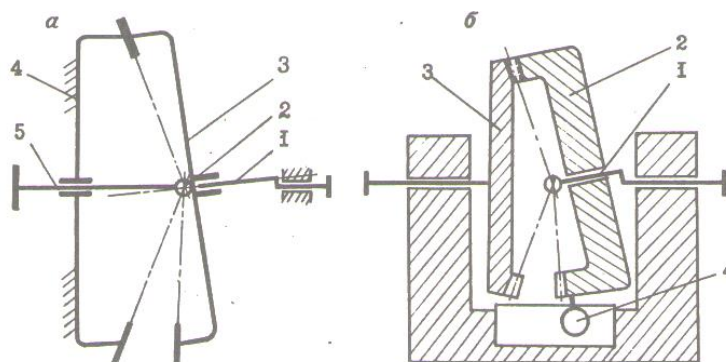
Волновые торцевые редукторы: а) с неподвижным центральным колесом; б) с сателлитным колесом
